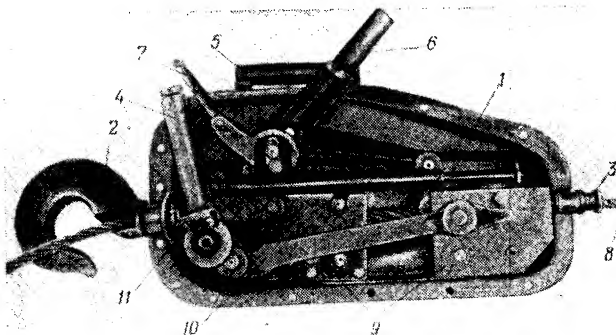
Механизм лебедки: 1 — крышка корпуса; 2 — крюк лебедки; 3 — направляющая втулка; 4 — рычаг переднего хода; 5 — рукоятка для переноса лебедки; 6 — рычаг заднего хода; 7 — защелка; 8 — трос лебедки; 9 — захваты; 10 — двуплечий рычаг; 11 — нажимные пружины.
